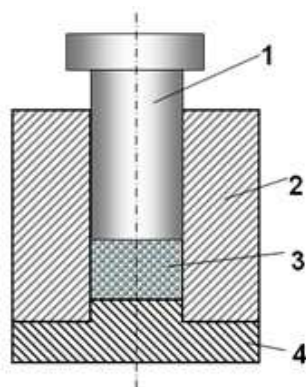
Схема пресс-формы для холодного прессования порошков
